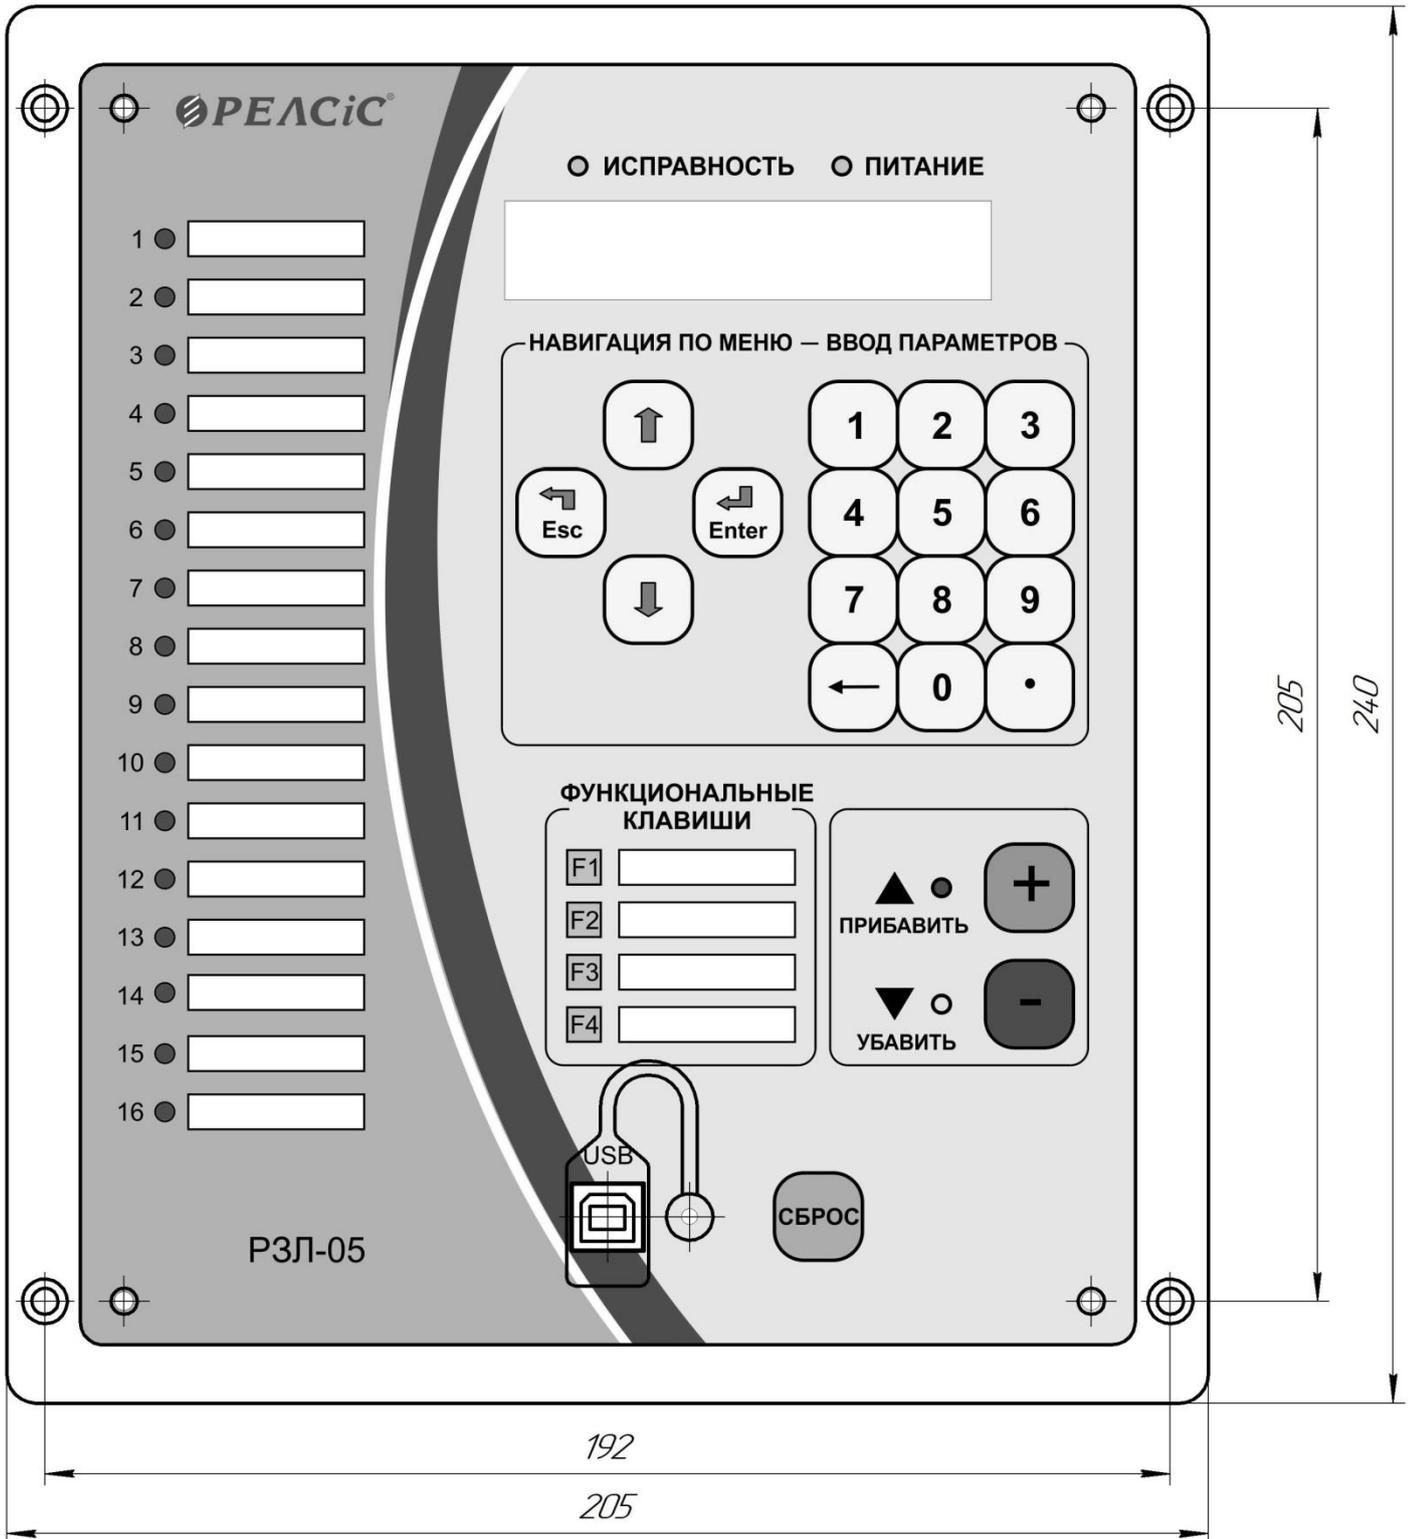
Габаритные размеры и установочный размеры и внешний вид передней панели устройств РЗЛ-05.РПН, РЗЛ-05.РПН01
